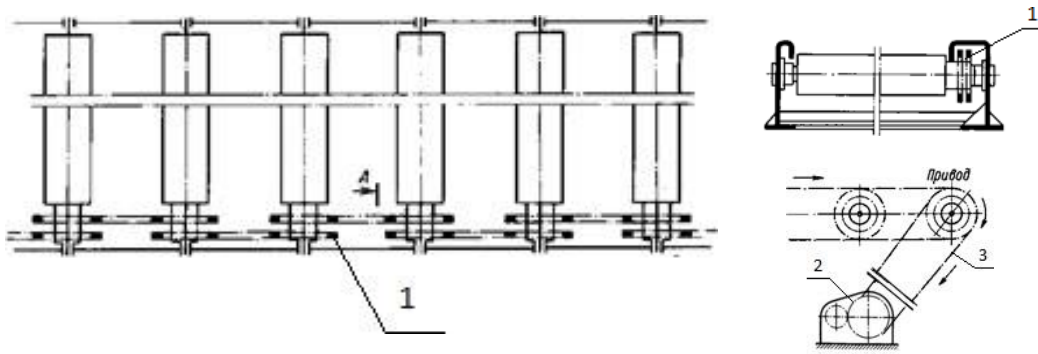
Кінематична схема роликового конвеєра, де 1) – тяговий між роликовий ланцюг, 2) – редуктор, 3) – тягова передача від редуктора до роликів.
